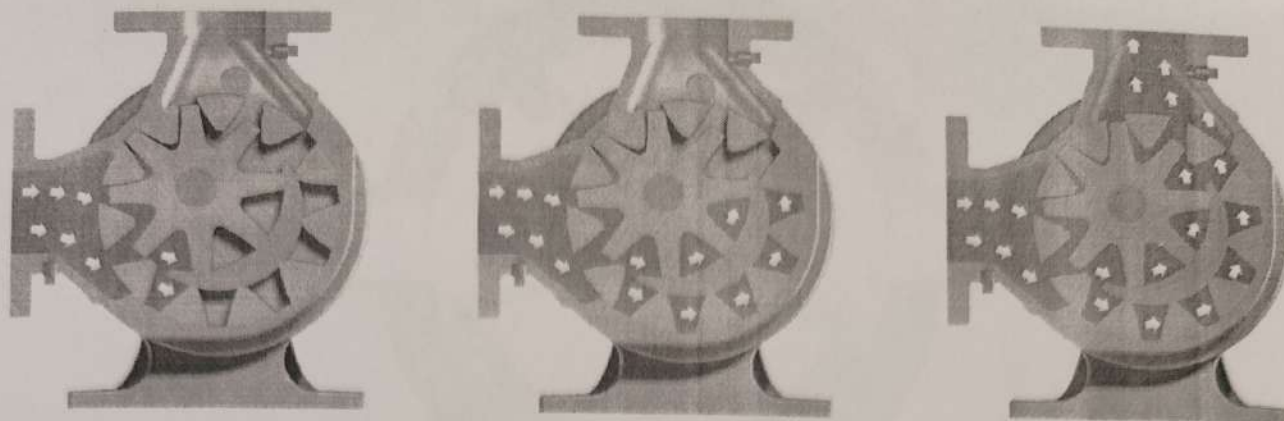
Шестеренчатый насос с внешним зацеплением
